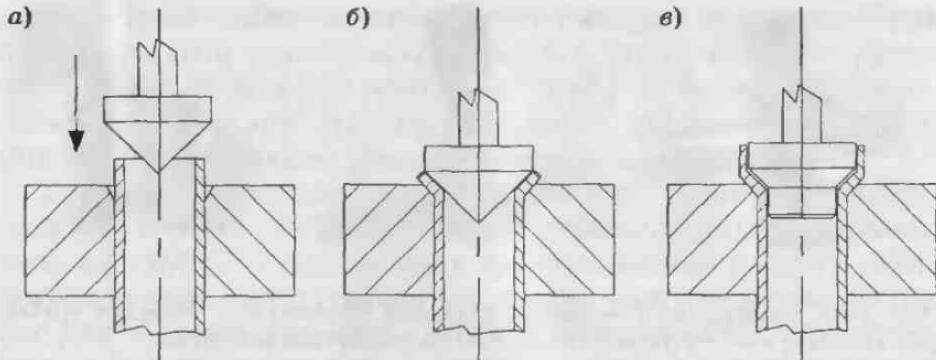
Схема бортования трубы: а — начало бортования; б — окончание бортования; в — использование труборасширителя
